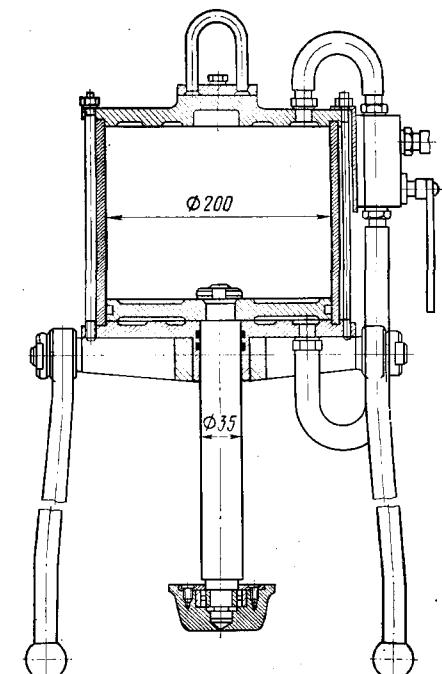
Пневматическое приспособление для сжатия пружин передней подвески
